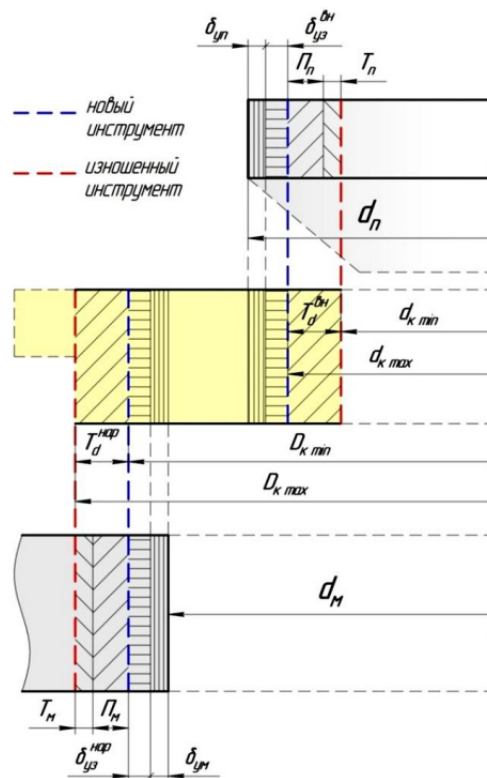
Схема полей допусков детали и инструмента
